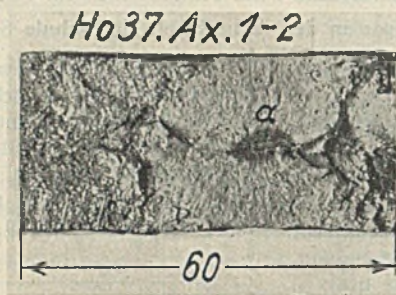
Bruchfläche einer X-Naht. Gasschmelzschweißung nach oftmals wiederholter Zugbelastung.
